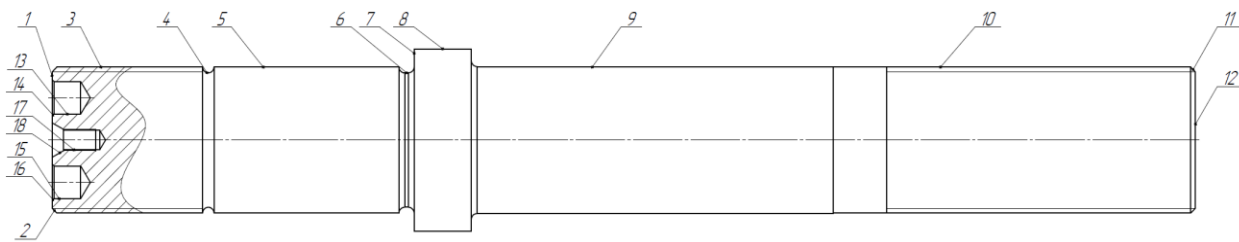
Нумерації поверхонь деталі “ Шток поршня 361-210002-2”
